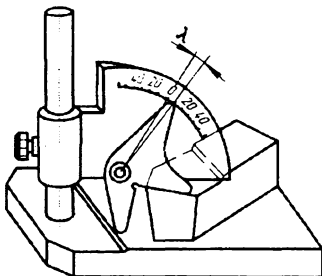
Схема измерения угла λ токарного проходного резца
